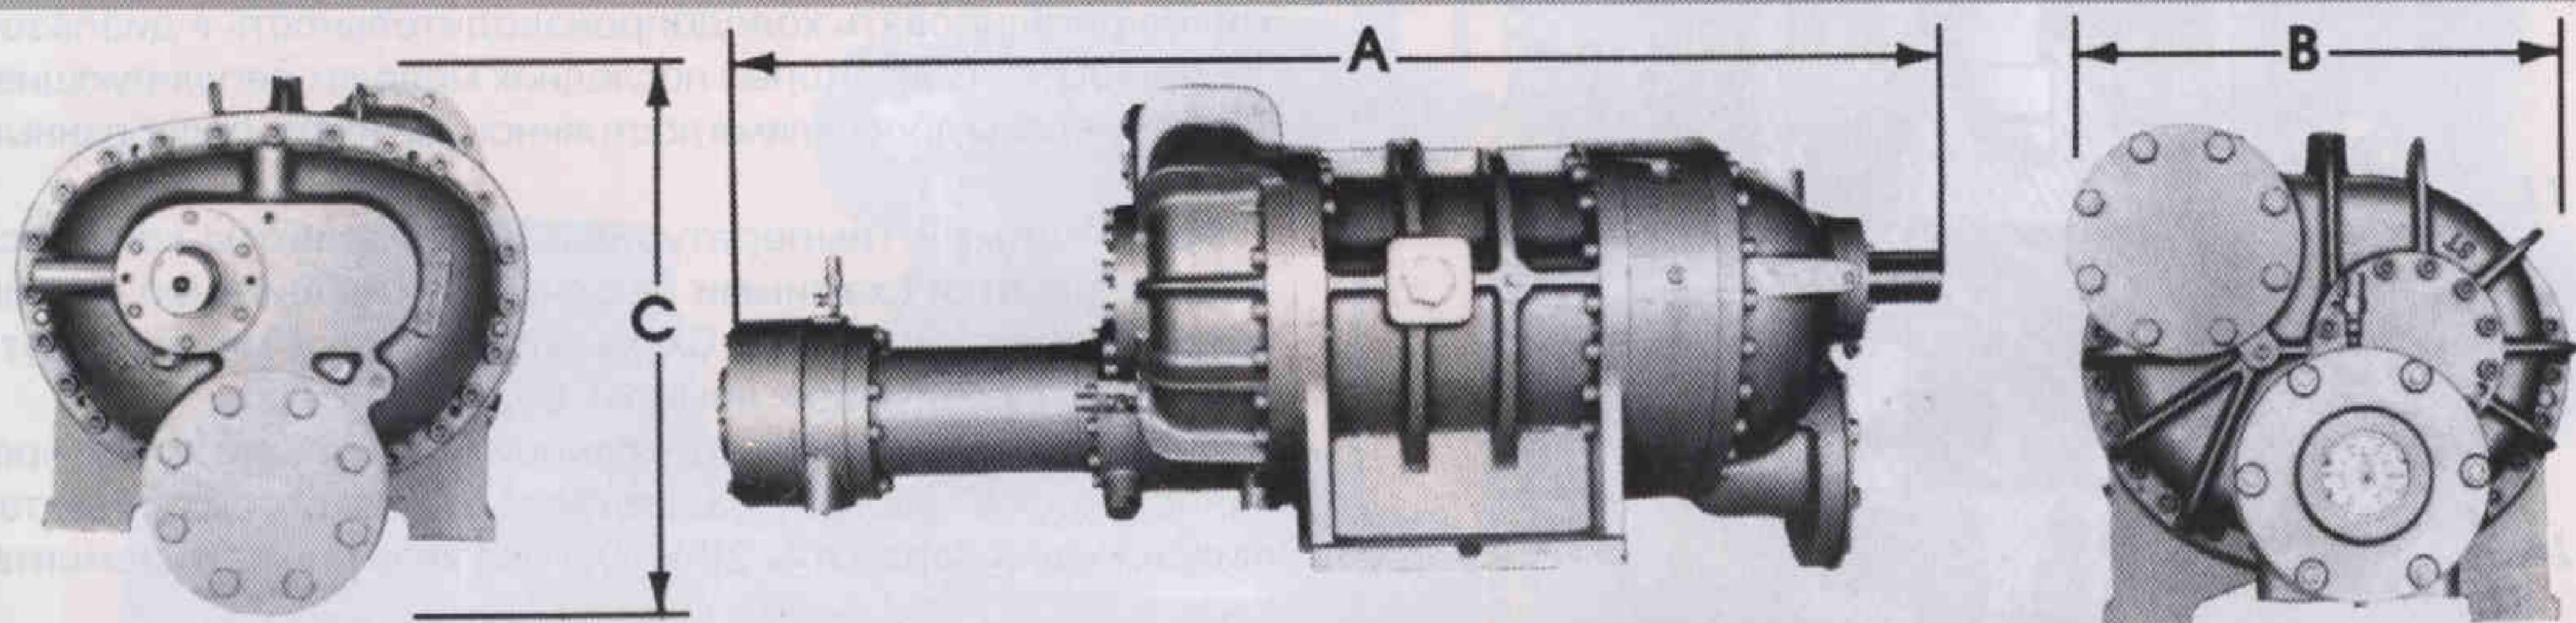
Компрессор типа LSC с приводом за четырехзубый ротор без встроенного насоса с индикатором положения золотника
